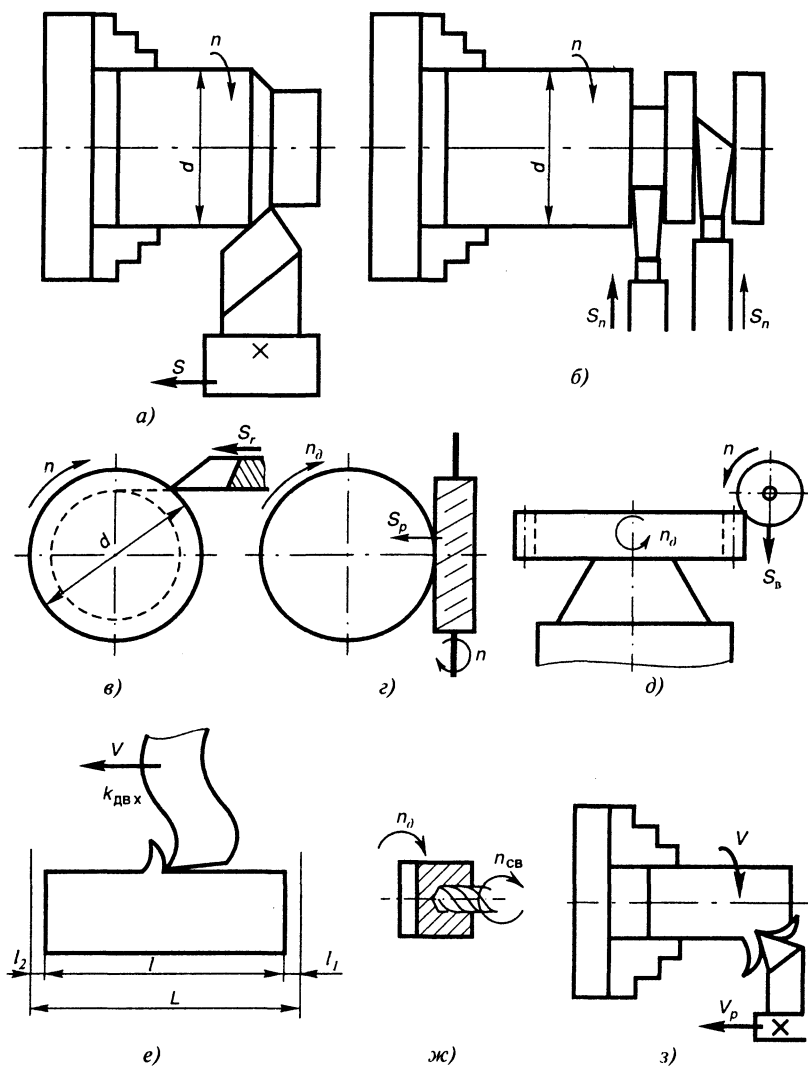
Виды главного движения и подачи в металлорежущих станках
